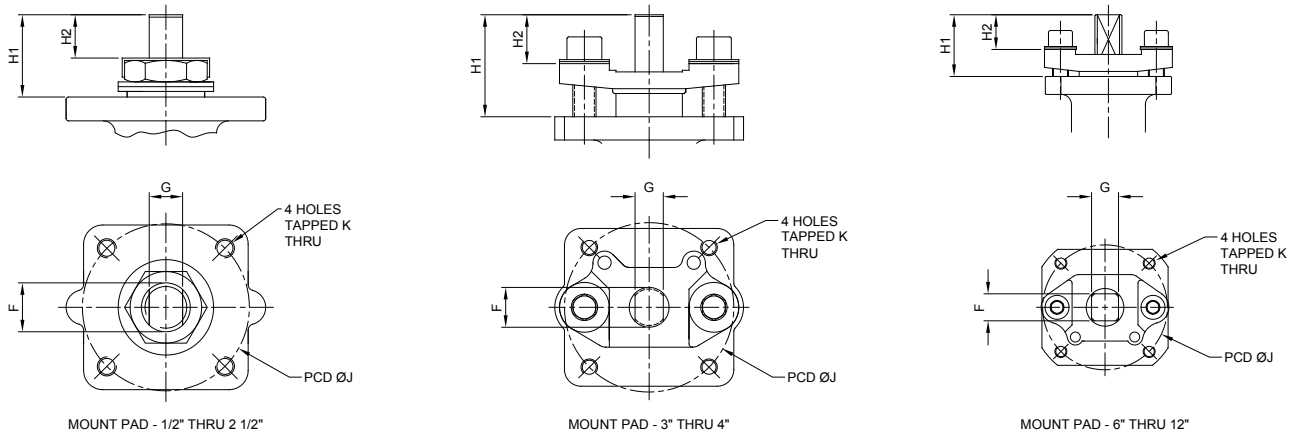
Configuración del Vástago de la Válvula y la Almohadilla de Montaje
